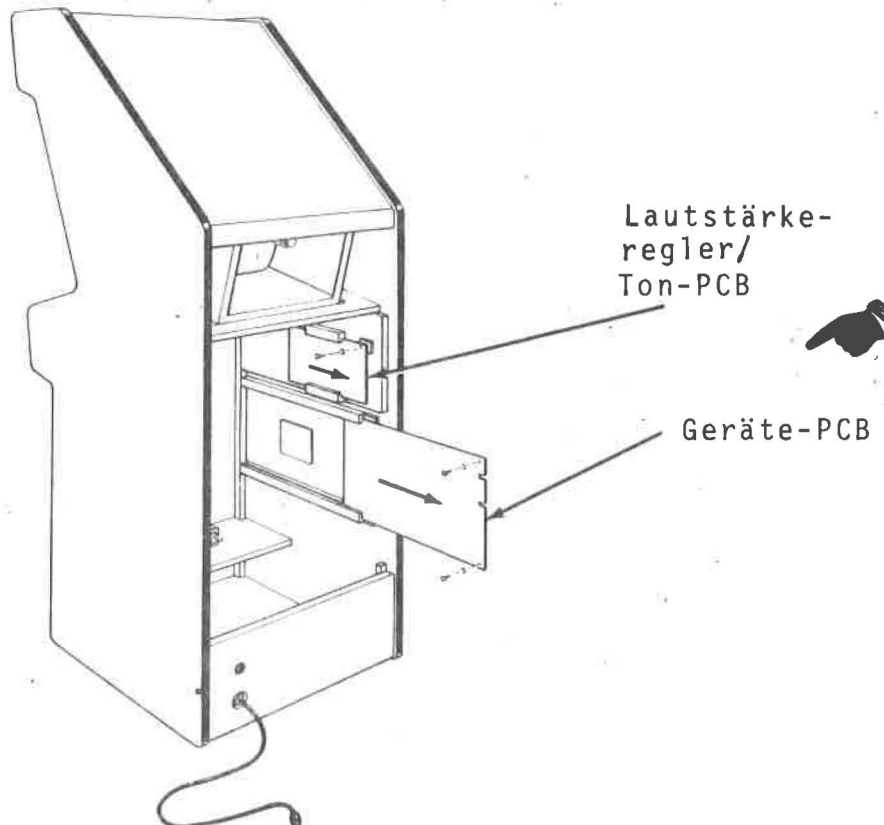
Auswechseln des Geräte- und Ton PCB's
